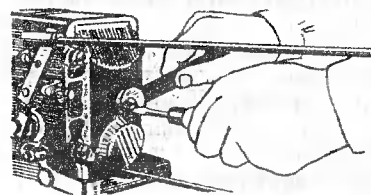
Вывертывание корпуса буферной пружины
